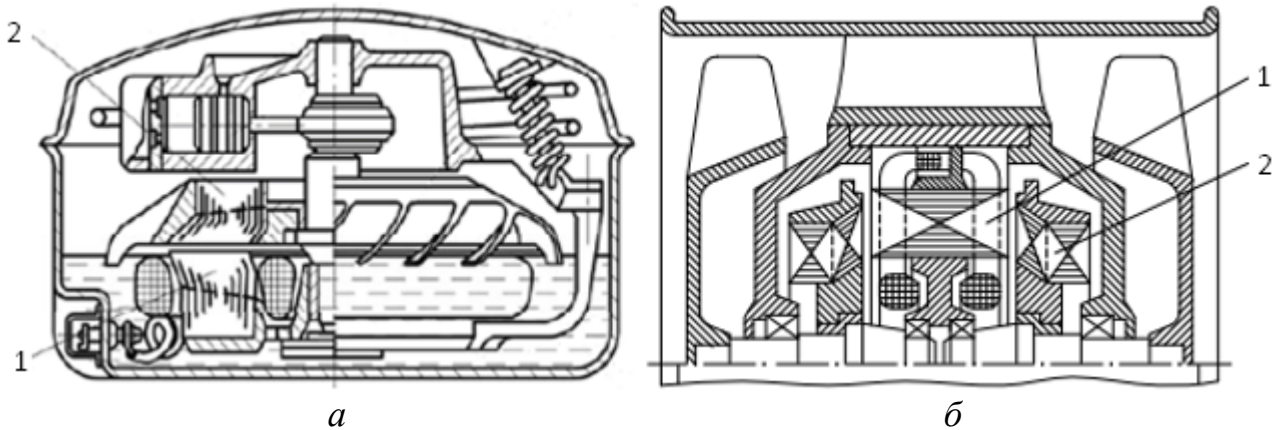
Приклади конструктивних схем механізмів герметичного компресора і осьового вентилятора з вбудованим однороторним (а) і двороторним зустрічного обертання (б) торцевими асинхронними двигунами: 1 – статор; 2 – ротор.
